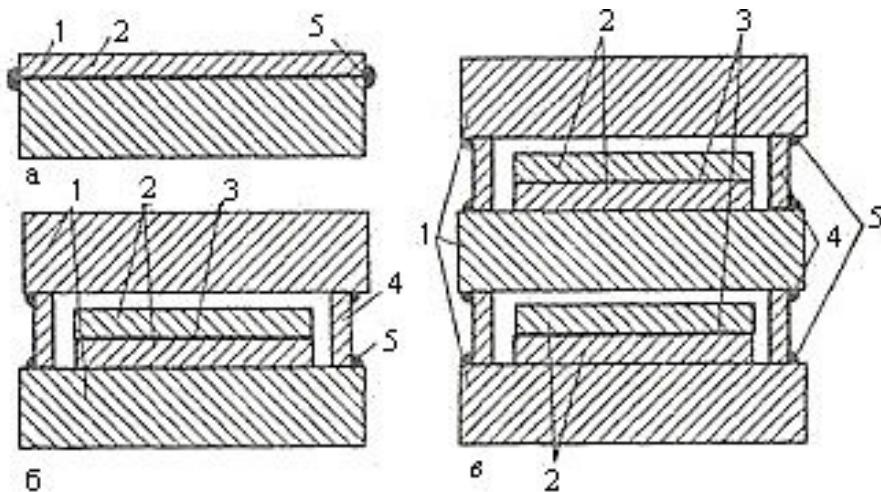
Конструкции пакетов для сварки прокаткой:
